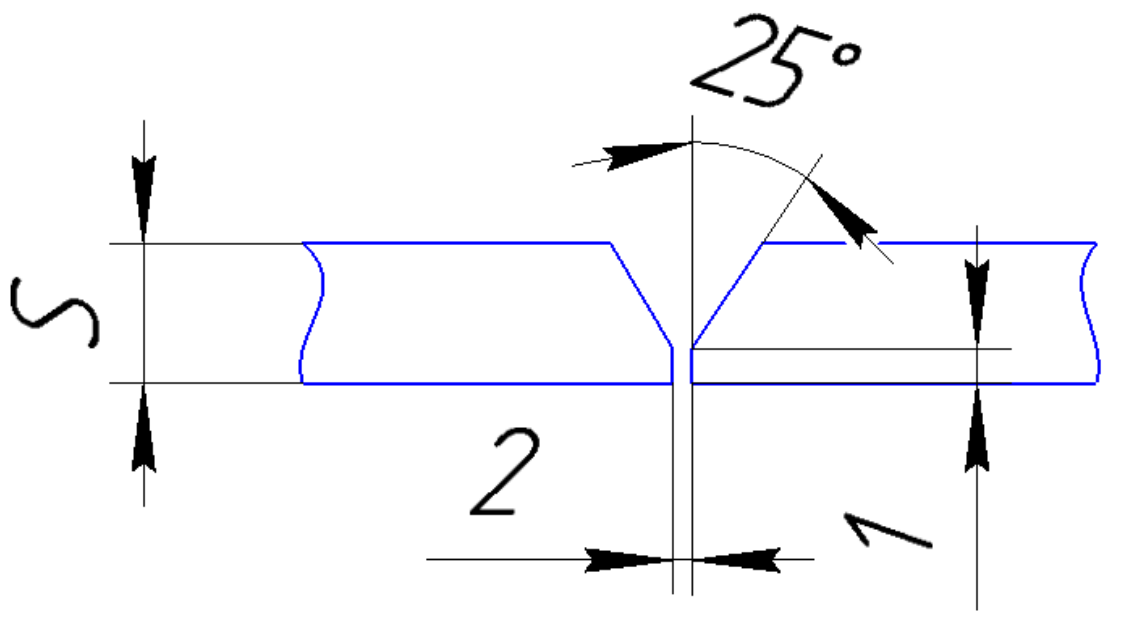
Подготовка кромок сварного соединения
